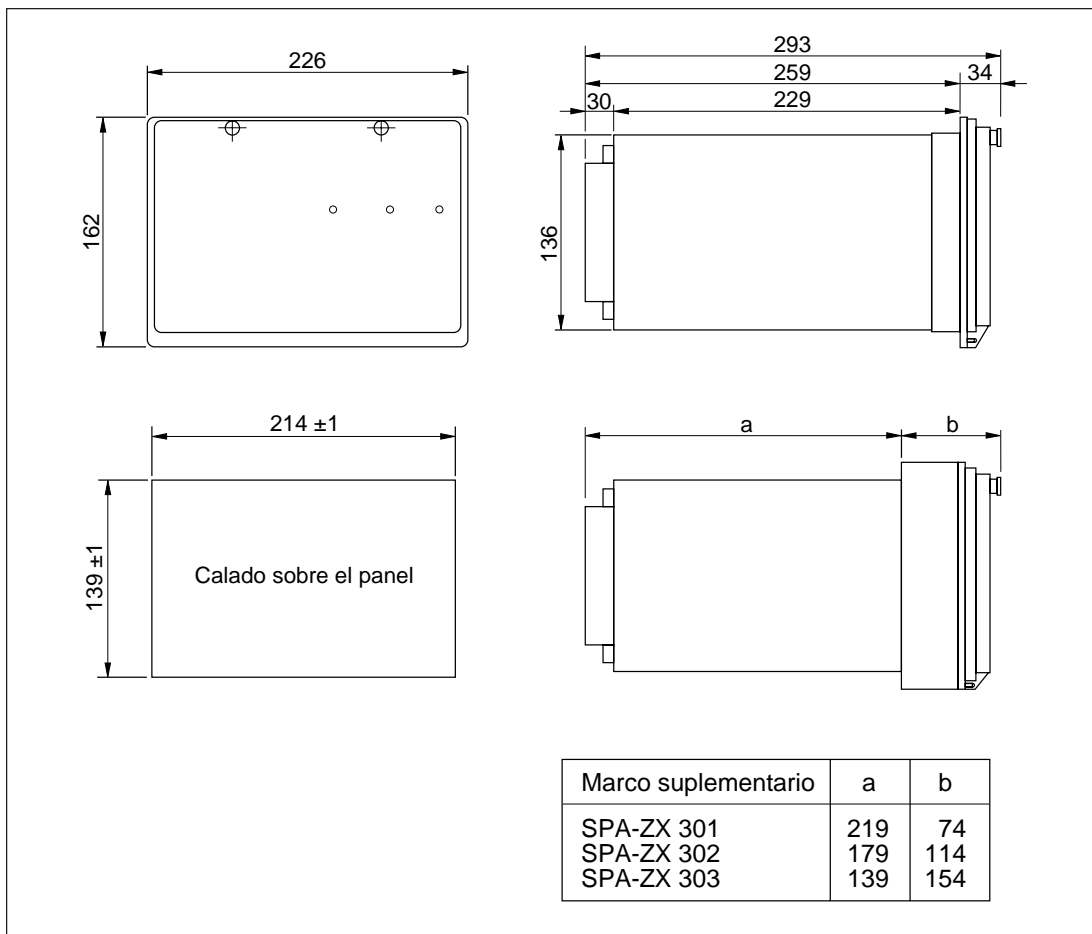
Planos de dimensiones y montaje del relé diferencial SPAD 346 C.
